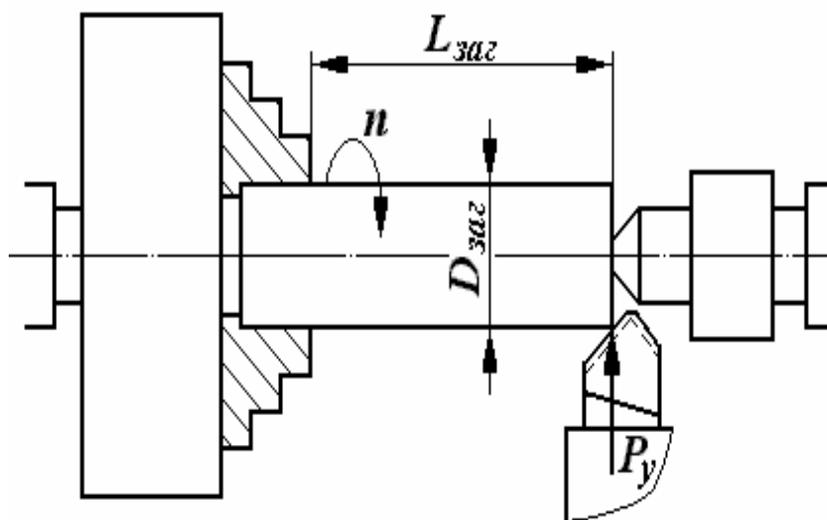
Схема установки заготовки в токарном патроне с поджатием центром задней бабки
